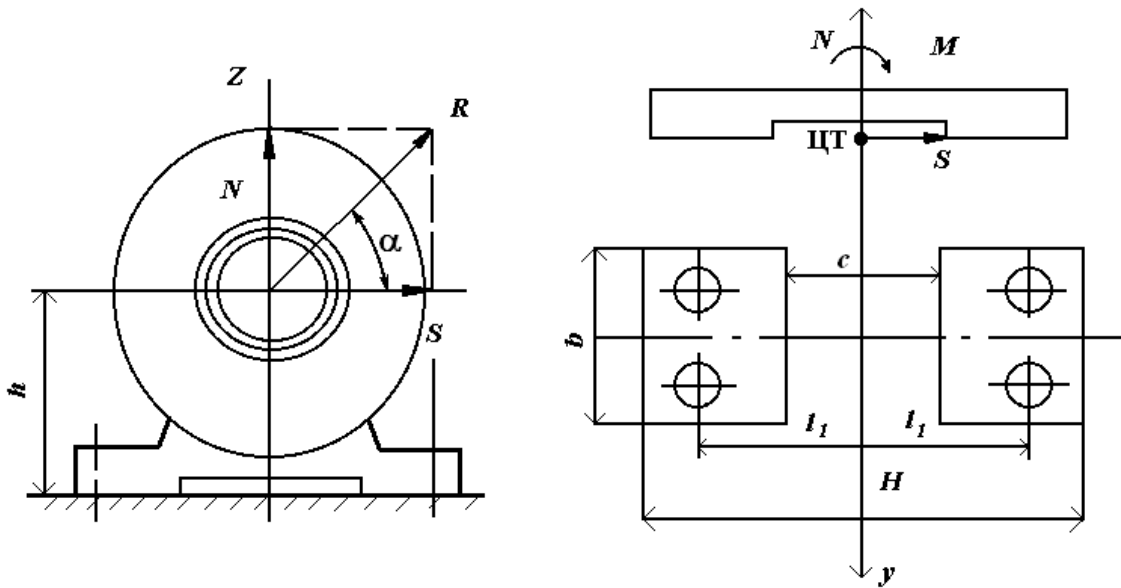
17. Схема к расчету болтов крепления корпуса подшипника
